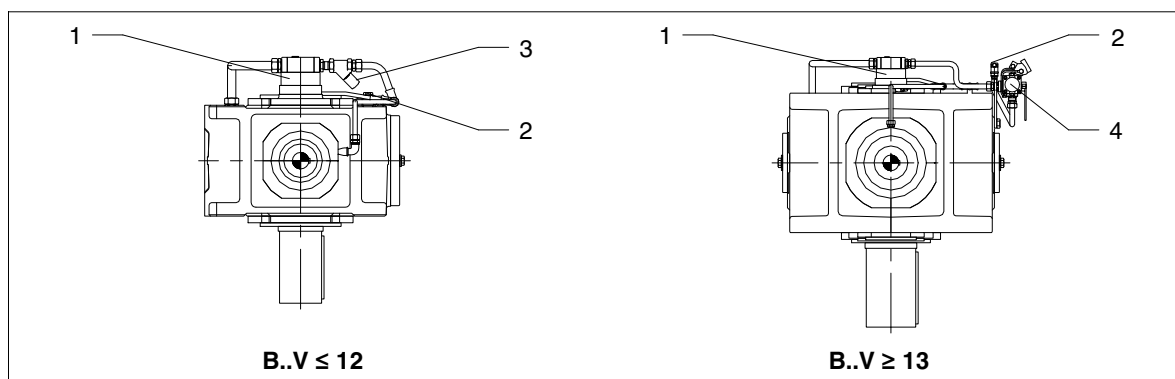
Sistema de alimentação de óleo montado com bomba flangeada no tipo B..V
